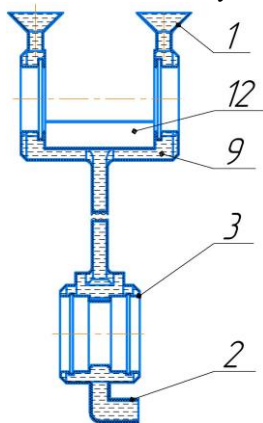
Композитная деталь рычаг с литниковыми элементами: 1 - выпор; 2 - литник; 3 – оболочковая форма; 9 – металлополимер; 12 – композитная деталь.
